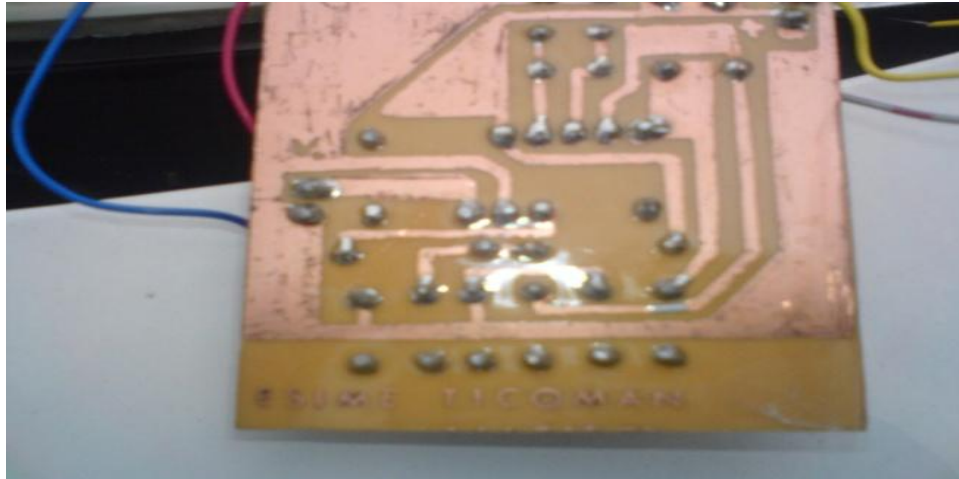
Lado de soldadura del circuito eléctrico del proyecto.
